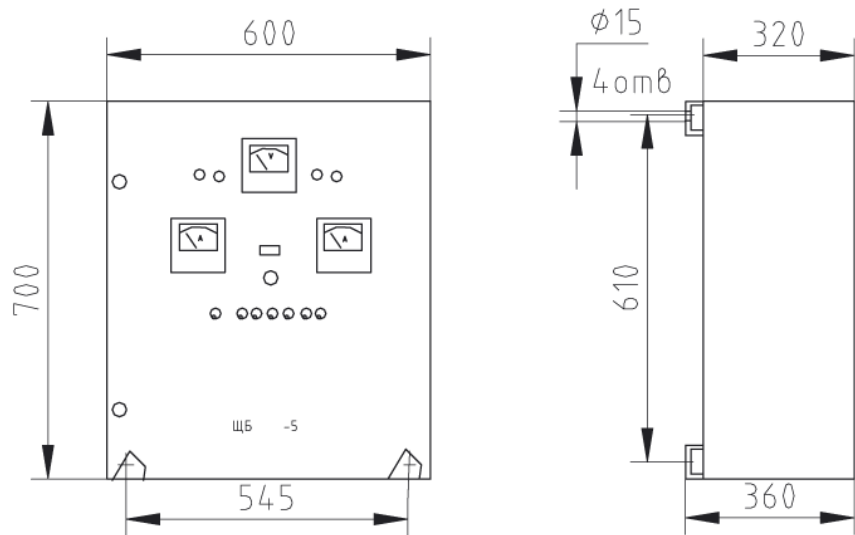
Габаритный чертёж щитов ЩБ 60/630-5, ЩБ 24/630-5
